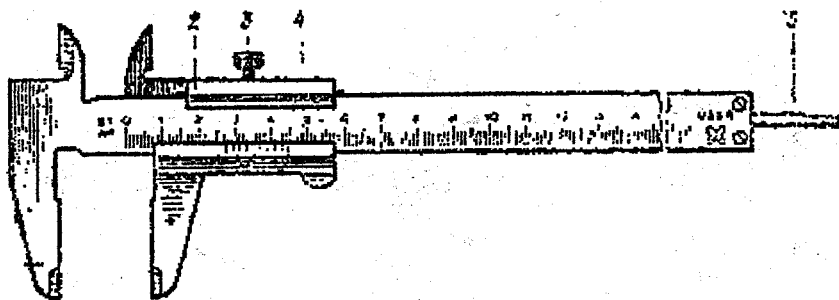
Штангенциркуль ШЦ-1:
